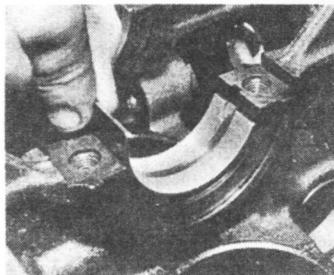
Установите верхние вкладыши коренных подшипников в блок цилиндров...
